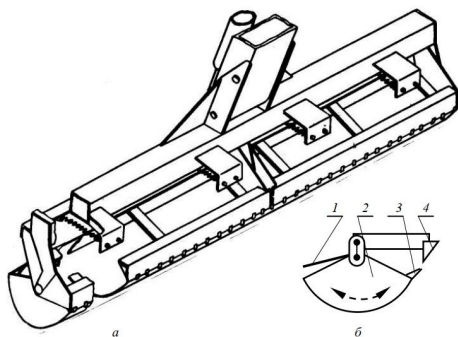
Уширенный поворотный ковш с неподвижной заслонкой и противорежущей кромкой: а – общий вид; б – схема работы; 1 – неподвижная заслонка; 2 – корпус ковша; 3 – кромка; 4 – противорежущая кромка.
